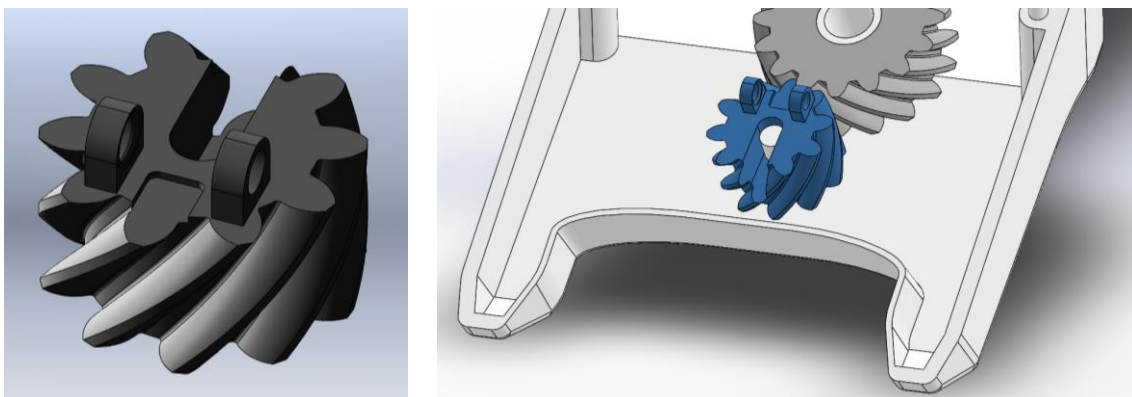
Detalle de los rebajes en la rueda (izq) y su colocación en el dispositivo (dcha)
